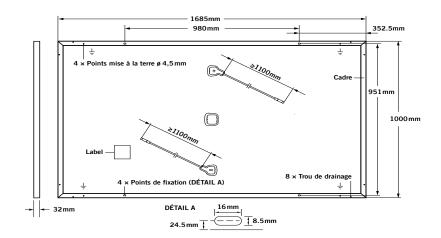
Dimensions externes (en mm) et composants pour Q.PEAK DUO-G5.X, Q.PEAK DUO BLK-G5.X,
